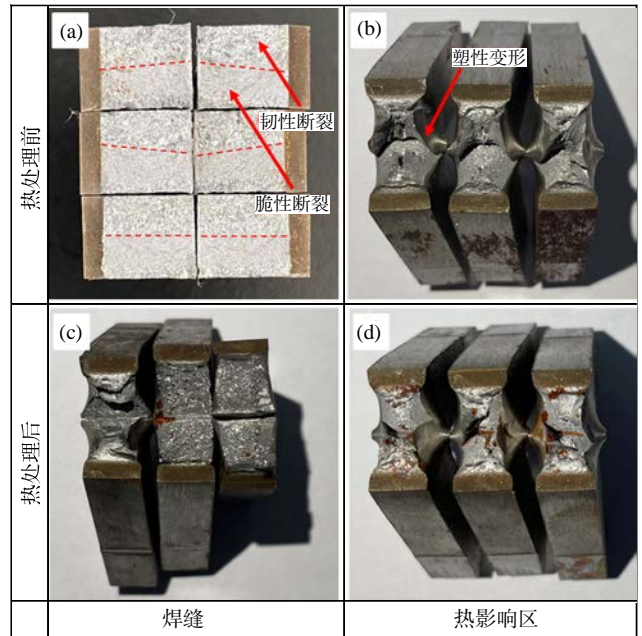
K-TIG 焊接接头冲击试样断口形貌
